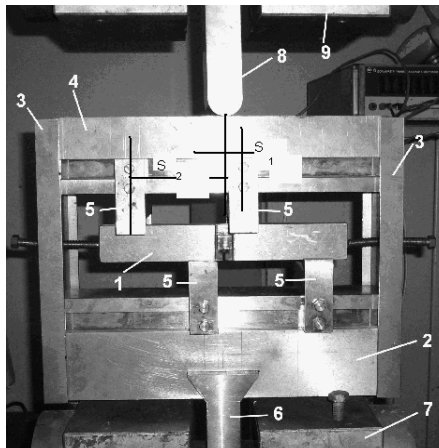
Приспособление для нагружения образца на несимметричный четырёхточечный изгиб
